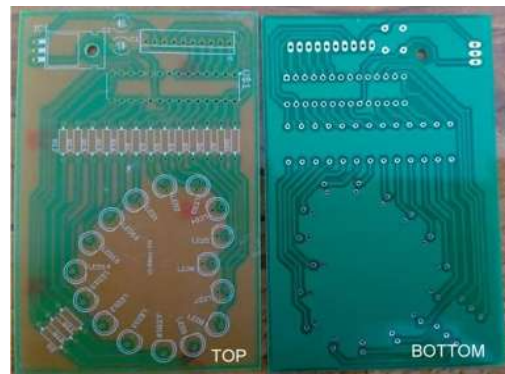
CAPAS TOP Y BOTTOM DE UNA PCB DE 1 CAPA DE COBRE
